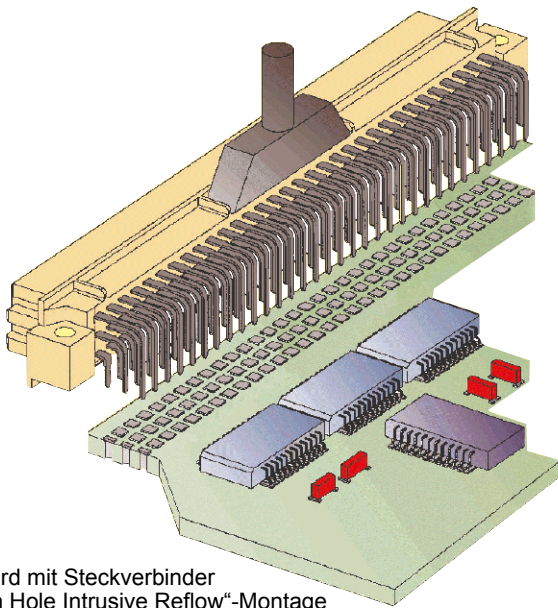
SMT-Board mit Steckverbinder für „Pin in Hole Intrusive Reflow“-Montage
